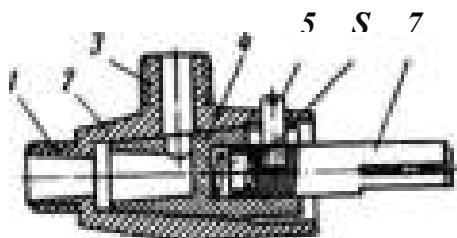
Унифицированный пробковый кран газовой плиты: 1 - штуцер для присоединения к газопроводу; 2 - корпус; 3 - штуцер для присоединения к коллектору; 4 - пробка; 5 - стопорный винт; 6 - пружина; 7 – стержень
